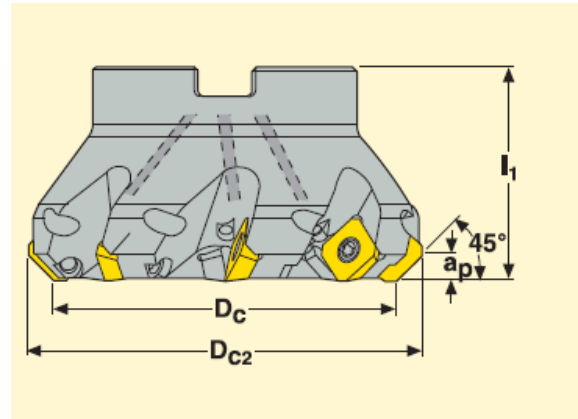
Фреза торцовая Ø80 R217.53 – 080-12-3А
